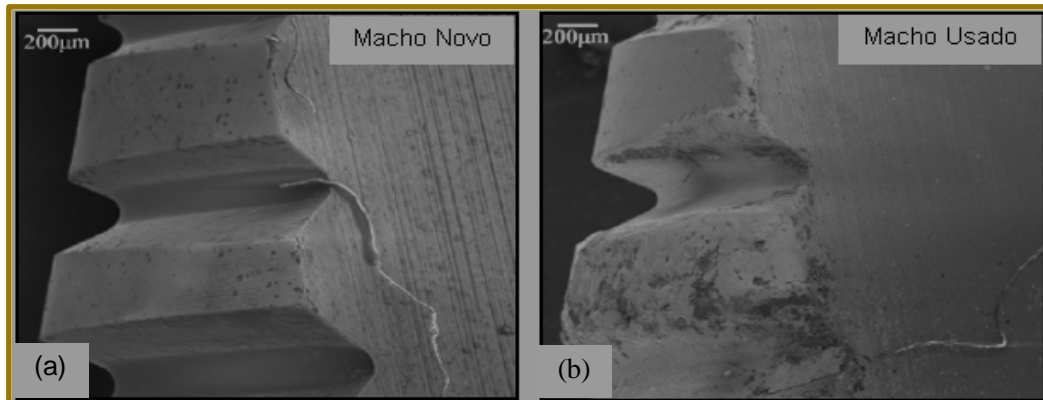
Desgaste apresentado no 3° e 4° filetes de dois machos de corte revestidos com TiAlN; a) Macho novo; b) Macho em fim de vida (BEZERRA, 2003)
